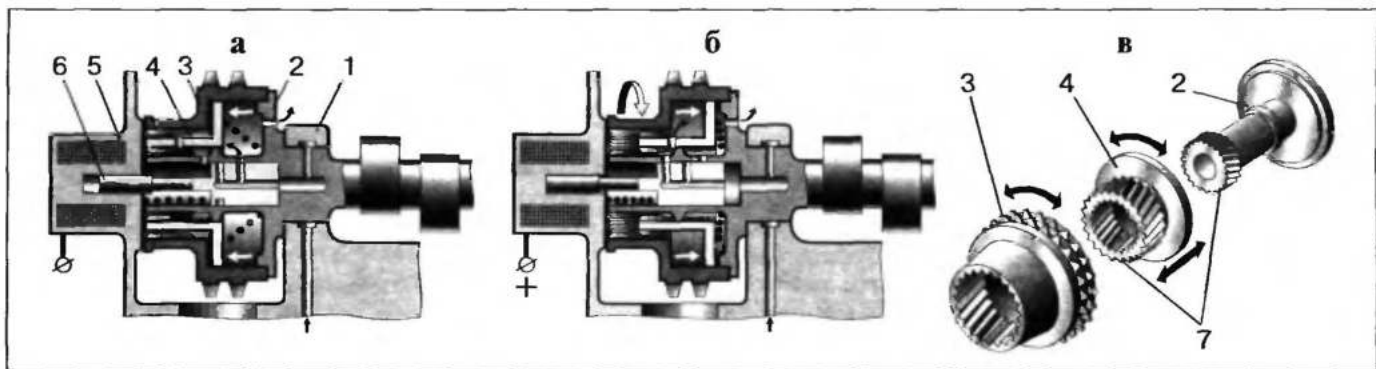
Схема устройства регулирования фаз газораспределения: 1 — головка блока; 2 — распределительный вал; 3 — звездочка привода распределительного вала; 4 — поршень; 5 — электромагнит; 6 — якорь-клапан; 7 — косозубые шлицы; а — поздние фазы — электромагнит выключен, поршень отжат влево давлением масла, поступающим через клапан; б — ранние фазы — электромагнит переводит клапан влево, поршень давлением масла перемещается вправо, "закручивая" звездочку относительно распределительного вала; в — соединение деталей устройства косозубыми шлицами
